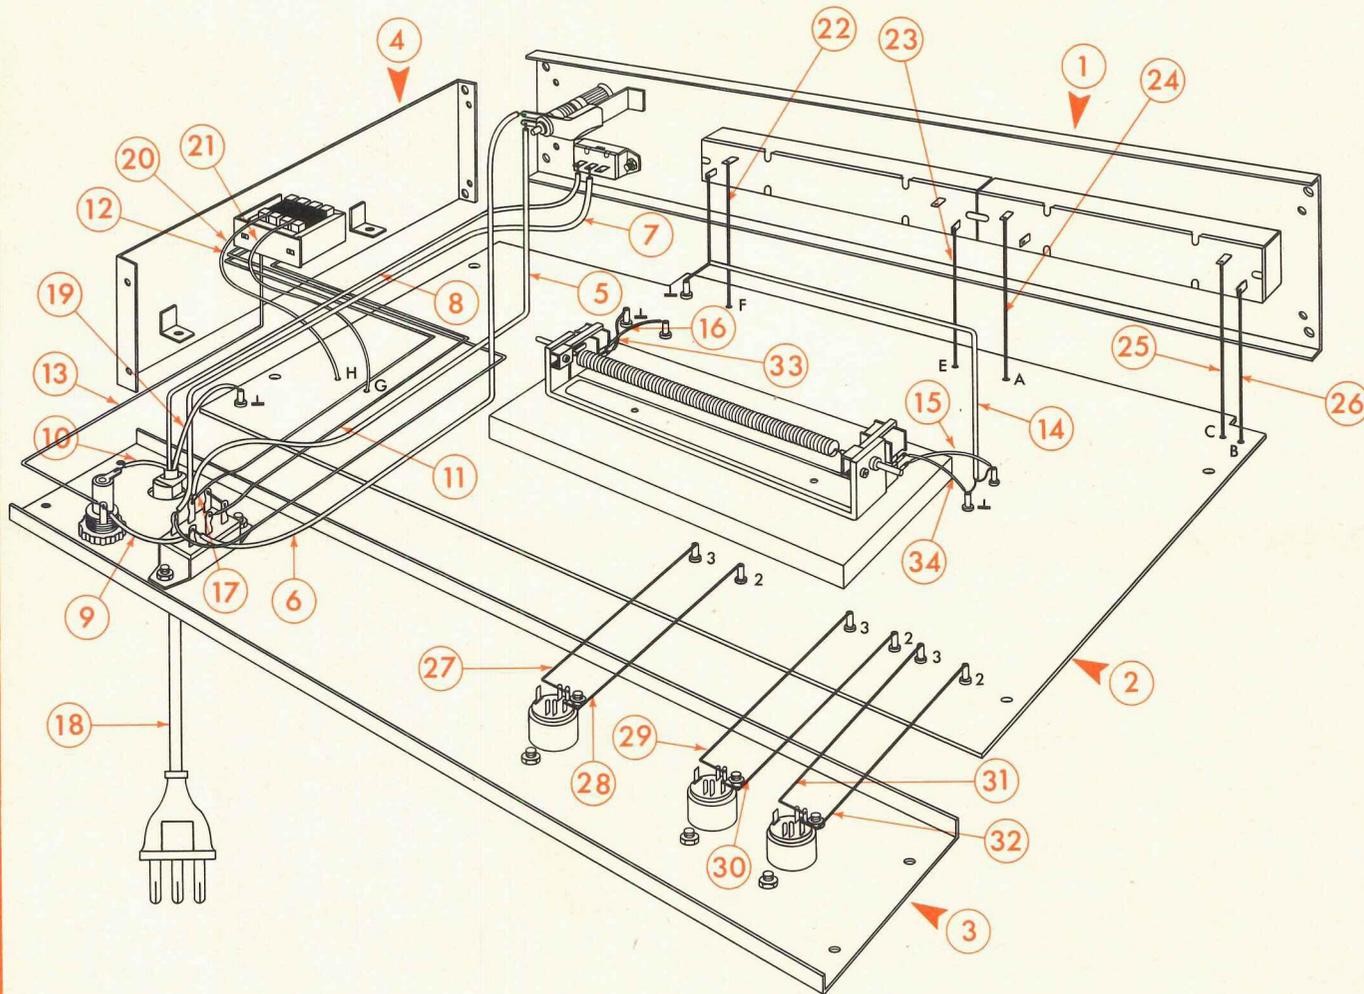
Esploso di montaggio dell'assieme dei pannelli e fissaggio del circuito stampato.
